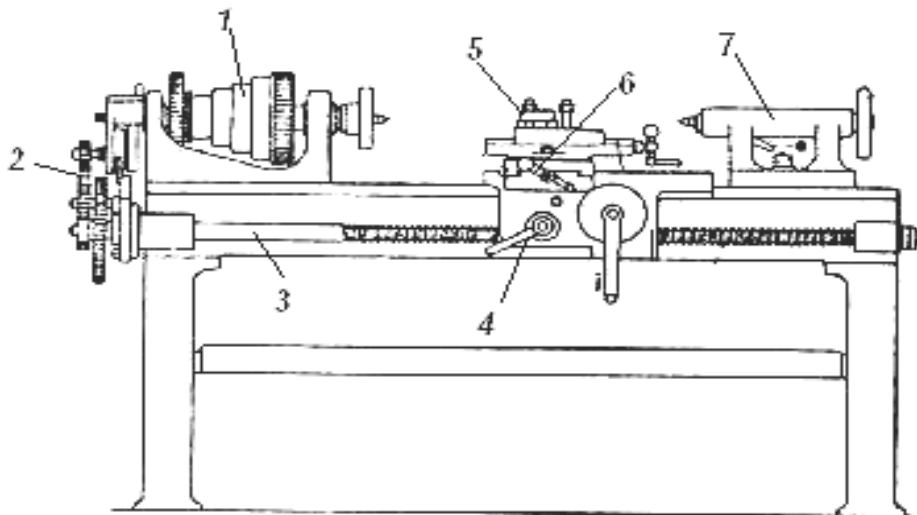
Токарный станок (конструктор Р. Робертс):
